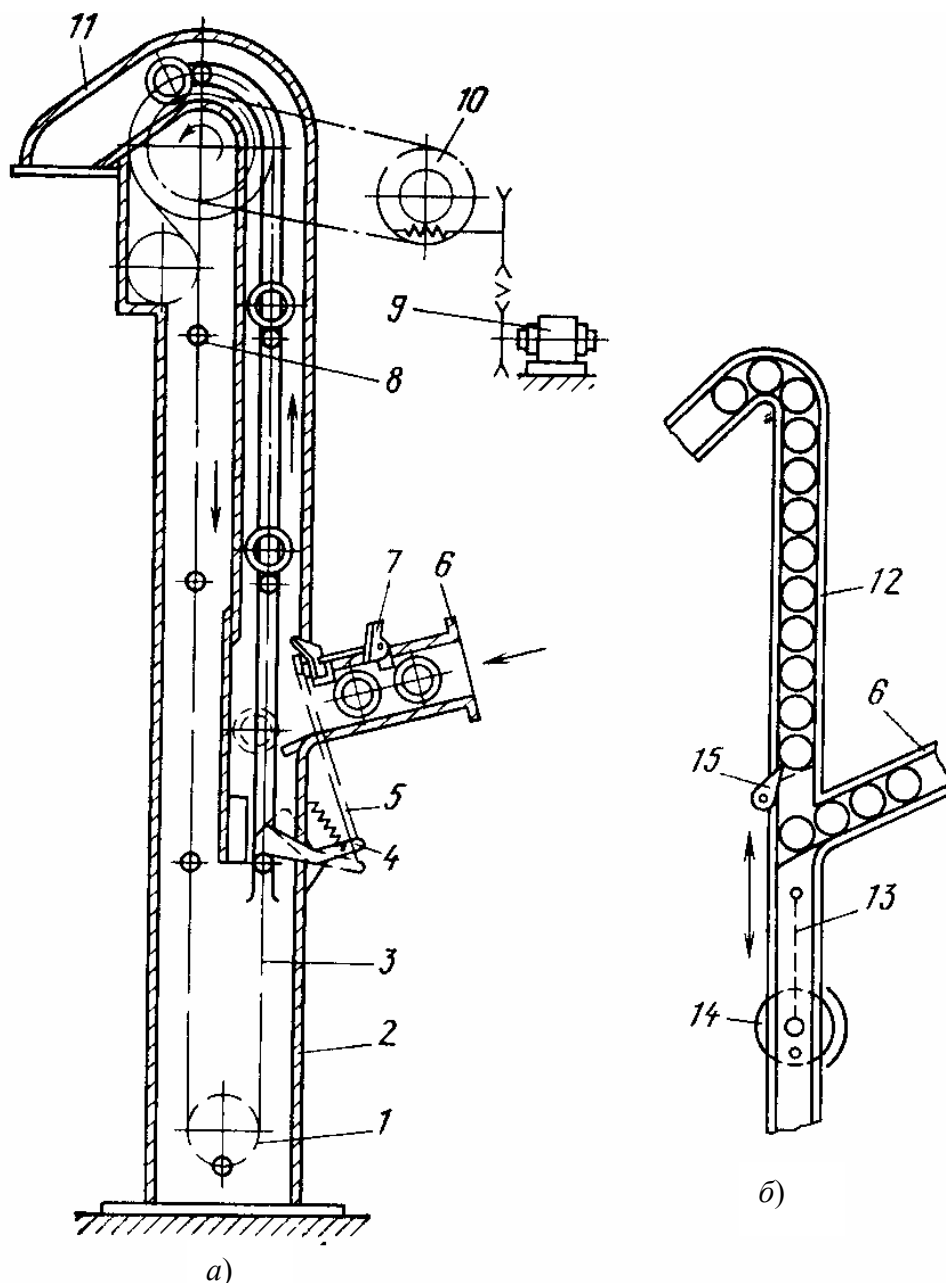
Подъемники: *а* – цепной; *б* – толкающий; 1 – натяжная звездочка; 2 – корпус; 3 – цепь; 4 – синхронизатор; 5 – тяга; 6 – приемный лоток; 7 – отсекатель; 8 – захват; 9 – электродвигатель; 10 – привод; 11 – лоток выдачи; 12 – шахта; 13 – толкатель; 14 – кривошипно-ползунный механизм; 15 – собачка
